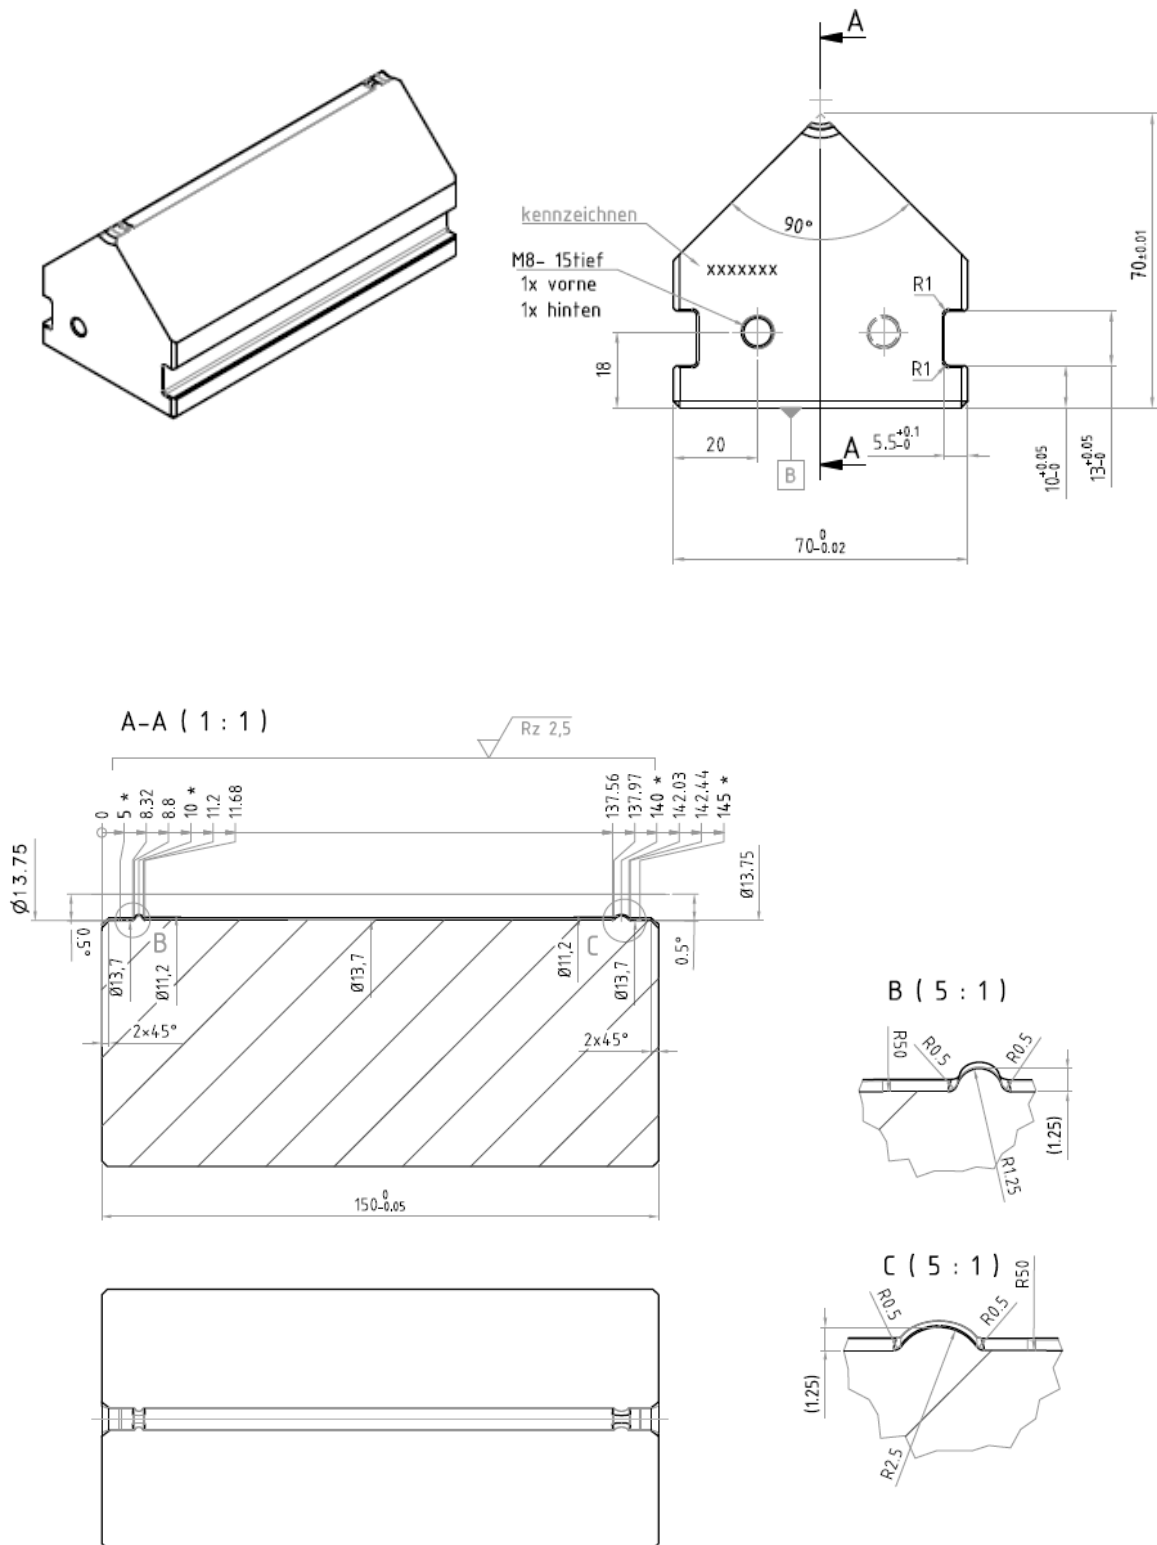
Technische Zeichnung des Werkzeugs für das Einstechrundkneten.
